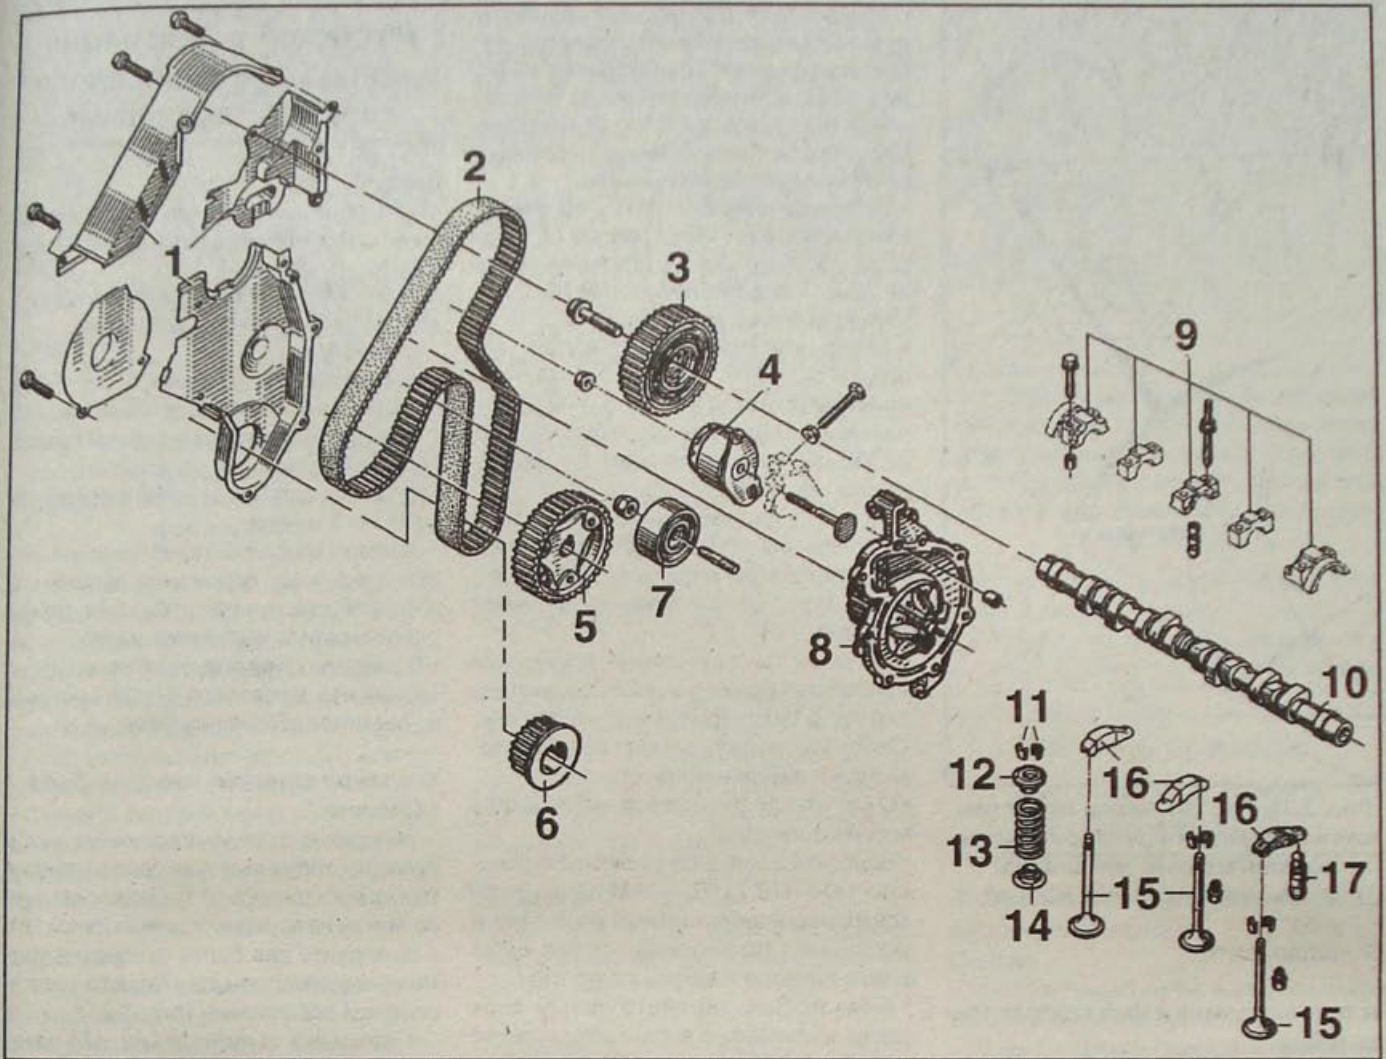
Зубчатый ремень привода газораспределительного механизма:
